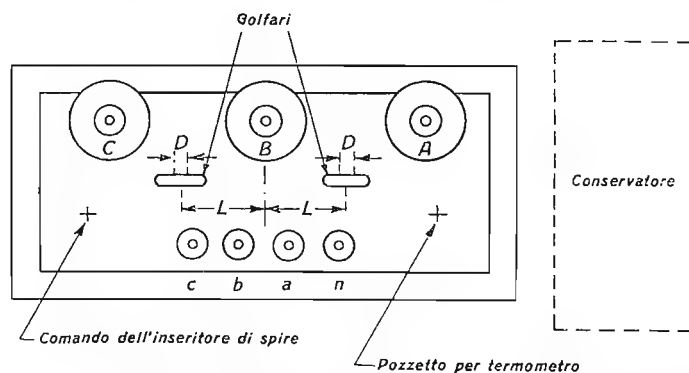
Disposizione degli elementi sul coperchio del trasformatore.
